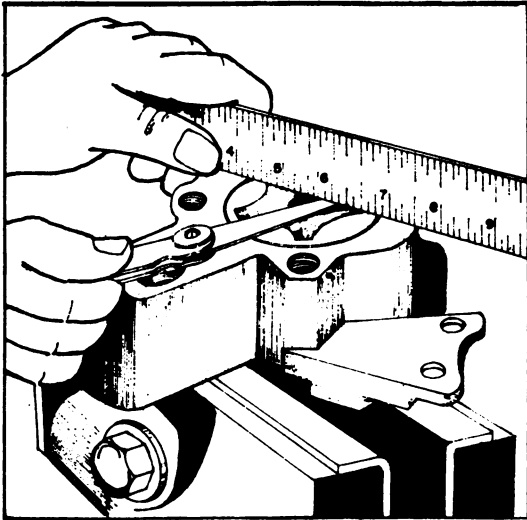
Luz entre la cara superior de los engranajes y la tapa de la bomba de aceite.
